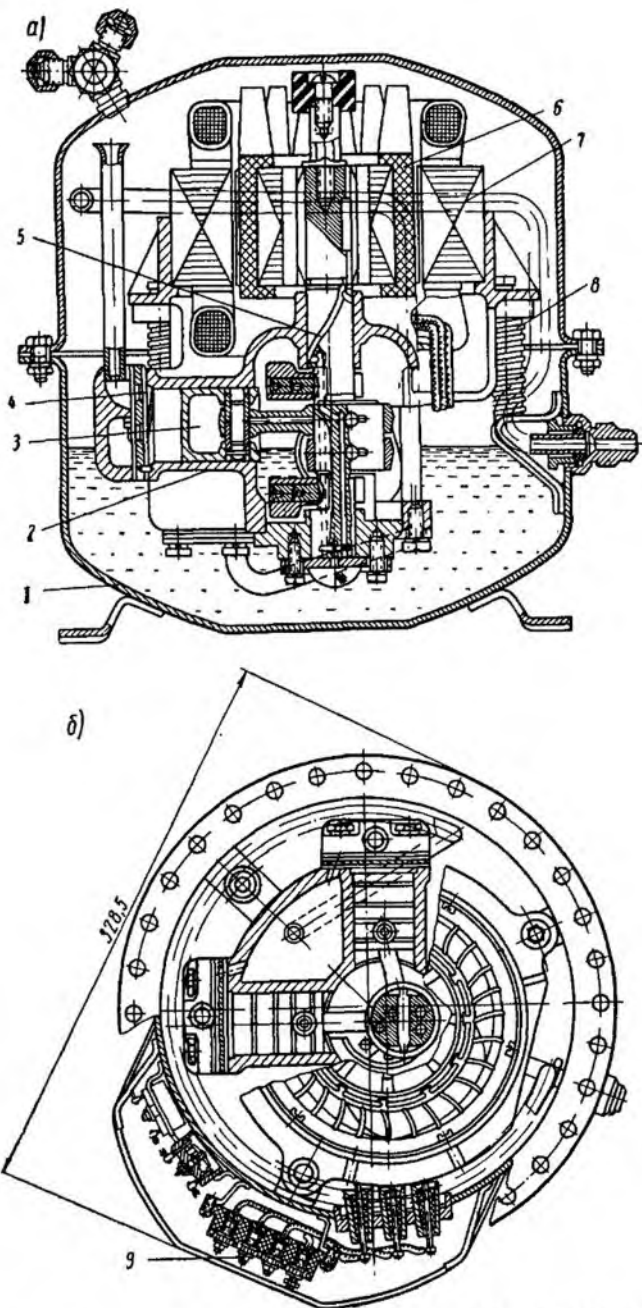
Герметичный фреоновый компрессор ФГ-0.7 ($Q_0=815 \text{ вт}$):
